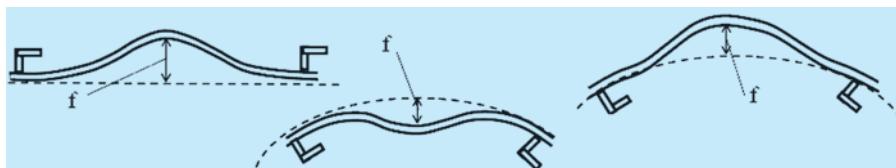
Схема измерения величины стрелки прогиба элемента корпуса
